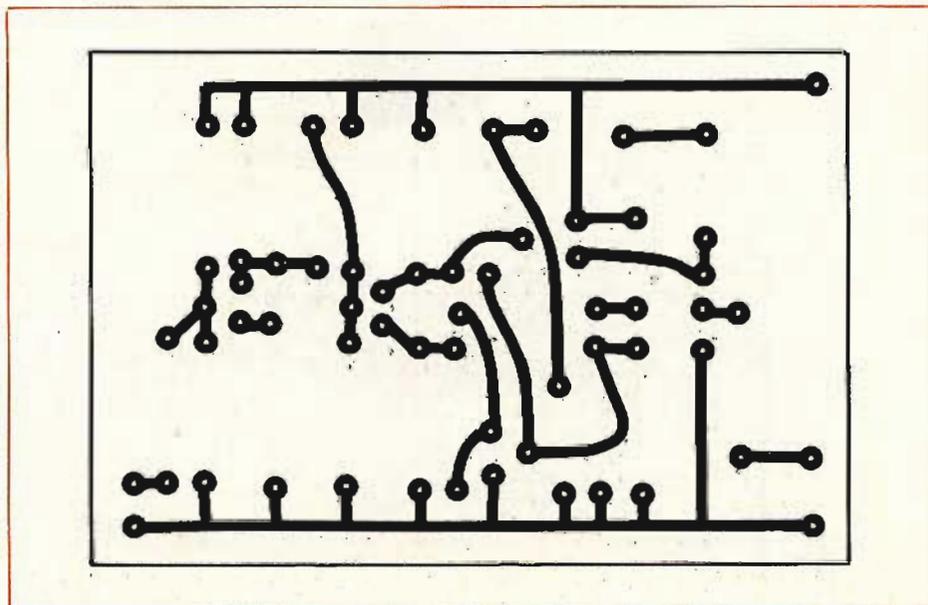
Circuito stampato del compressore visto dal lato rame.
